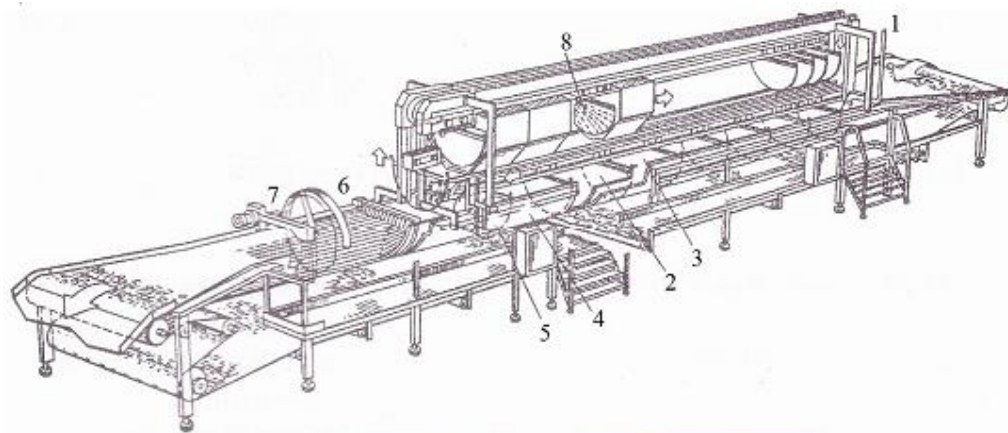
Апарат безпервної дії фірми Алрта для виготовлення сирного зерна: 1 - впускна труба; 2 - зона сквашування; 3 - жолобоподібний стрічковий транспортер; 4 - робоча ємність; 5 - електростатичний відділювач згустку; 6 – пристрій для розрізання пласту (горизонтальний); 7 - пристрій для поперечного розрізання пласту; 8 - пристрій для очищення розділювальних перегородок
